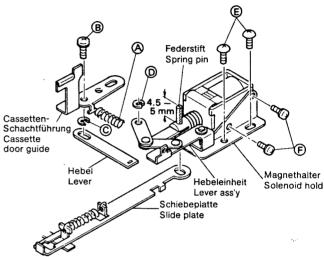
Magnet der Capstan-Andruckrolle Fig. 3-17 Pinch solenoid replacement
